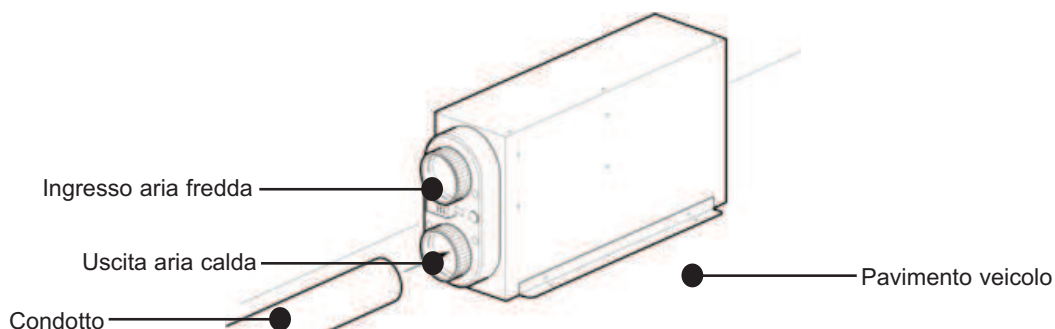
Installazione all'interno – Connessione al condotto dell'aria calda
